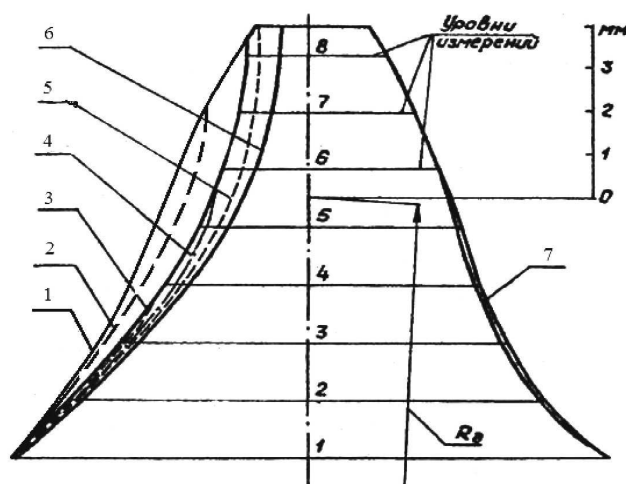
Формы профиля зуба ведущей звездочки, изменяющиеся в процессе эксплуатации базовой передачи:
